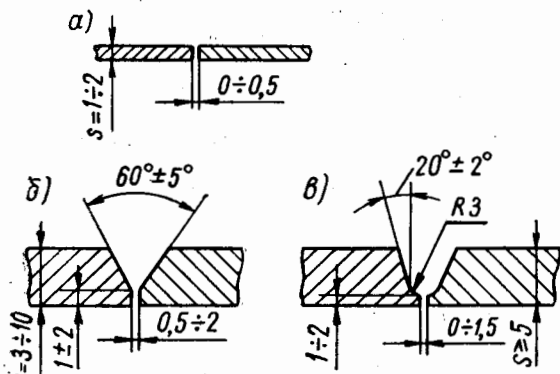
Конструктивные элементы подготовки кромок листовой стали марки 0X17H16M3T, свариваемой ручной аргоно-дуговой сваркой неплавящимся (вольфрамовым) электродом: а — без разделки кромок; б — V-образная разделка кромок; в — V-образная разделка с криволинейным скосом кромок
